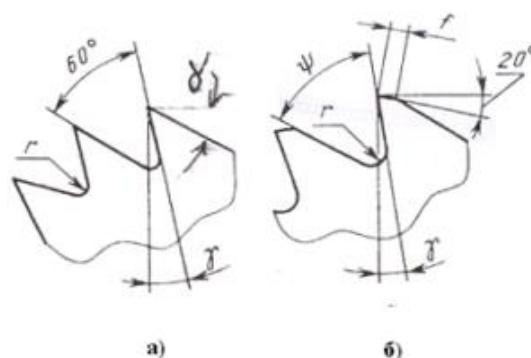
Формы зуба отрезной фрезы; без ленточки (а); с ленточкой(б)
